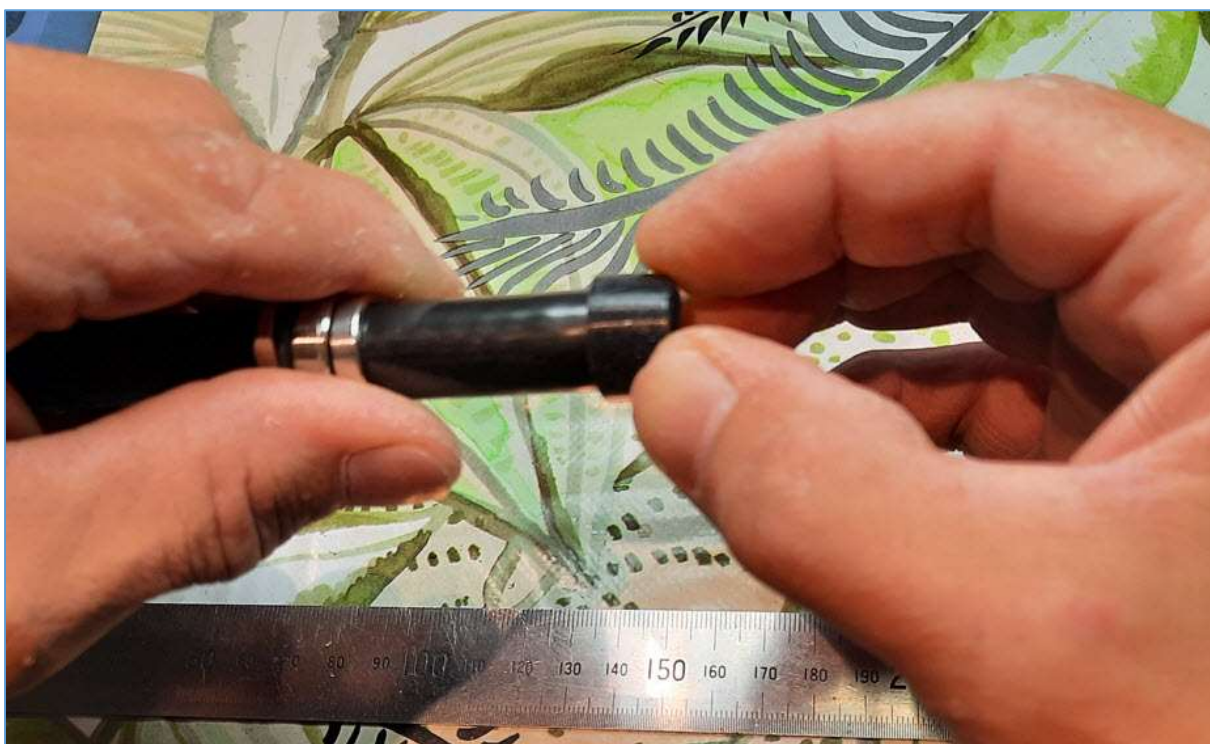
Ensuite enfiler le manchon en caoutchouc du presse-étoupe du connecteur. Photo : ON4IJ.
